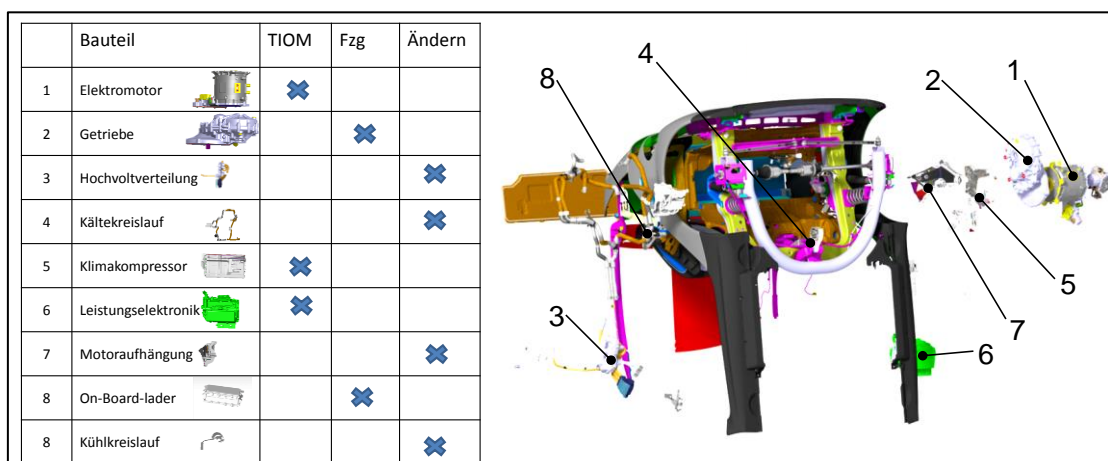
links: Übersicht der im Demonstratorfahrzeug verbauten Komponenten; rechts: Packaging der Komponenten im Ursprungsfahrzeug
